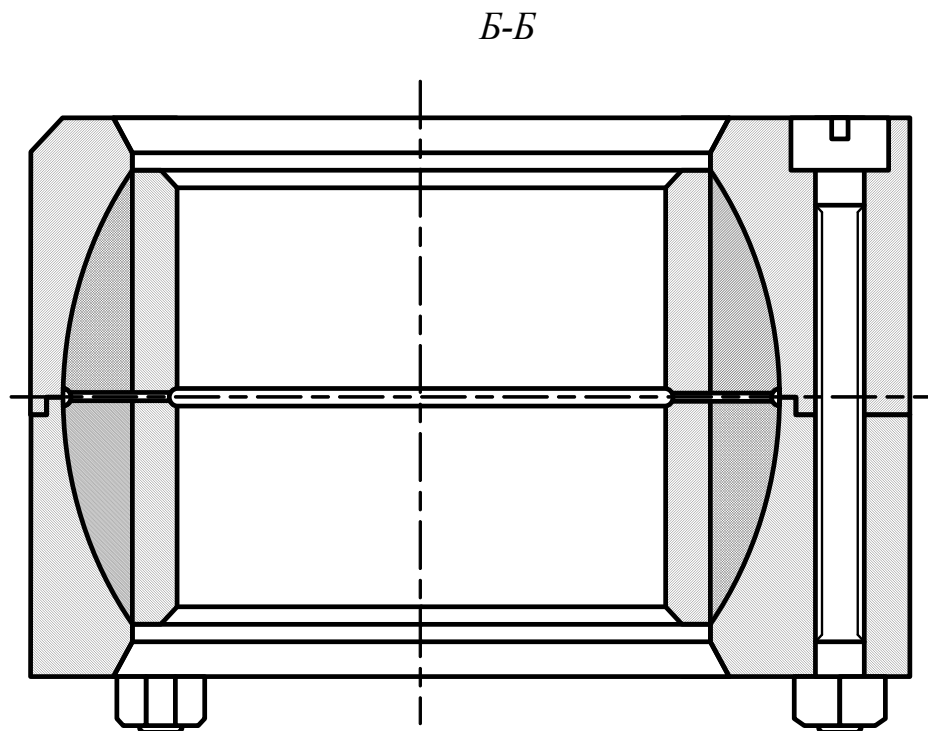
Шарнірний механізм (перетин Б-Б рис. 2.4)
